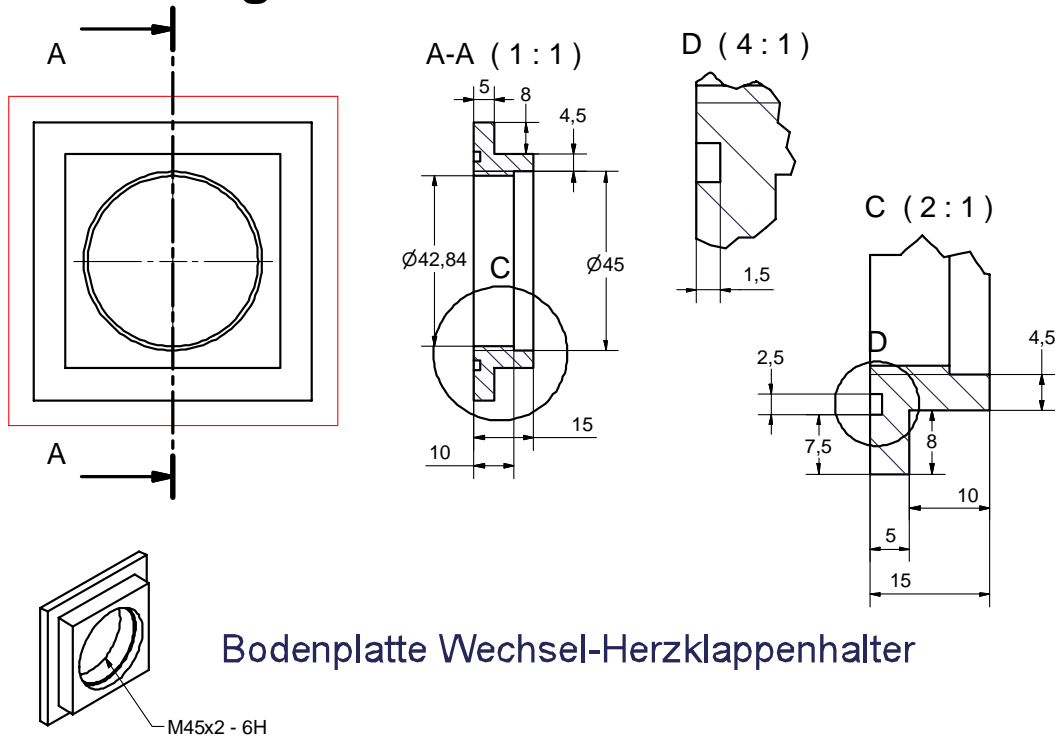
Maßzeichnung der Bodenplatte des neuen Probenhalter.
